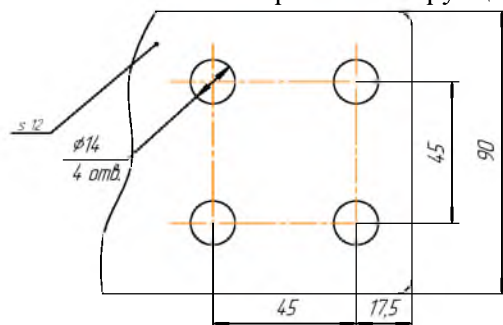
Разметка отверстий для присоединения подводящих проводов для РГП СЭЦ® -110/2000
